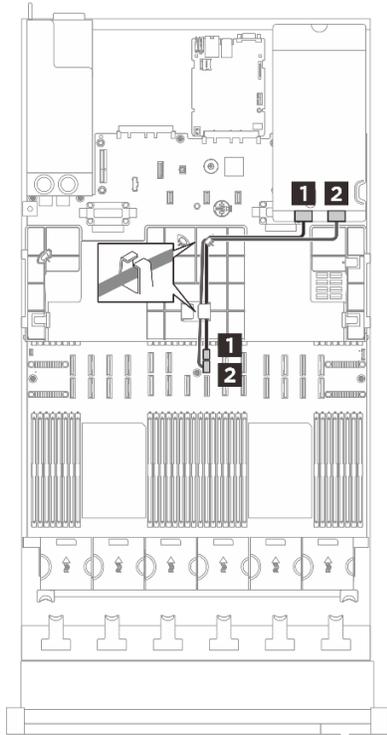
Disposición de los cables para la placa posterior de la unidad M.2 posterior
